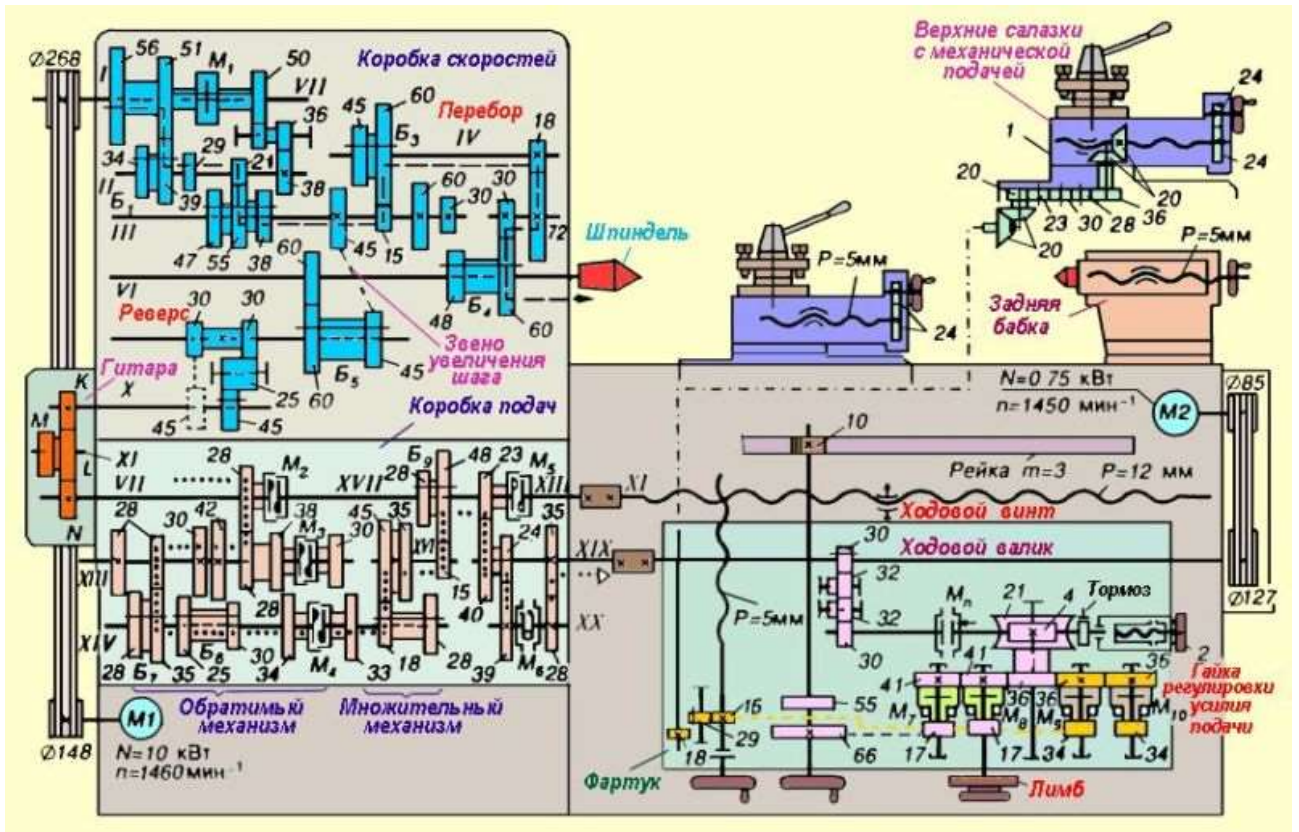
Кінематична схема токарно-гвинторізного верстата
